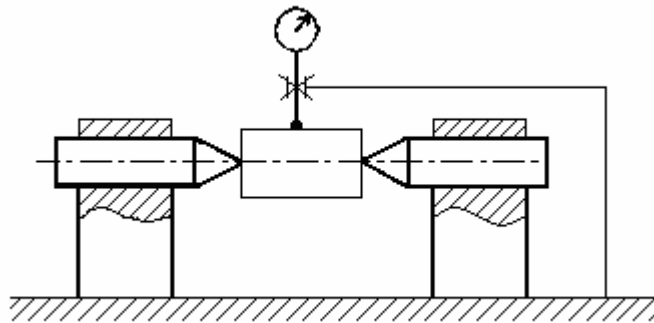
Базирование цилиндрических деталей в центрах
